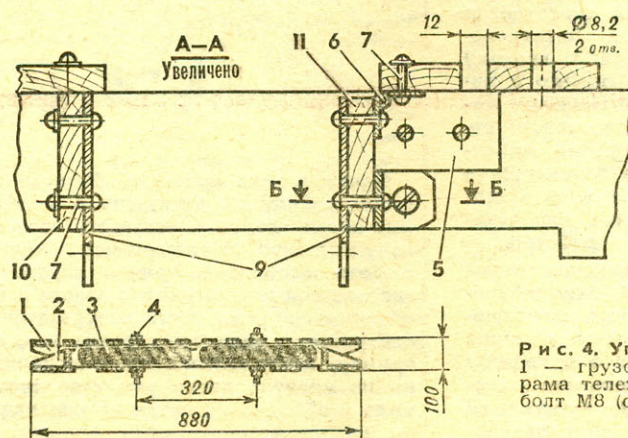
Упаковка колес: 1 — грузовая платформа, 2 — рама тележки, 3 — колесо, 4 — болт М8 (ось колеса).
